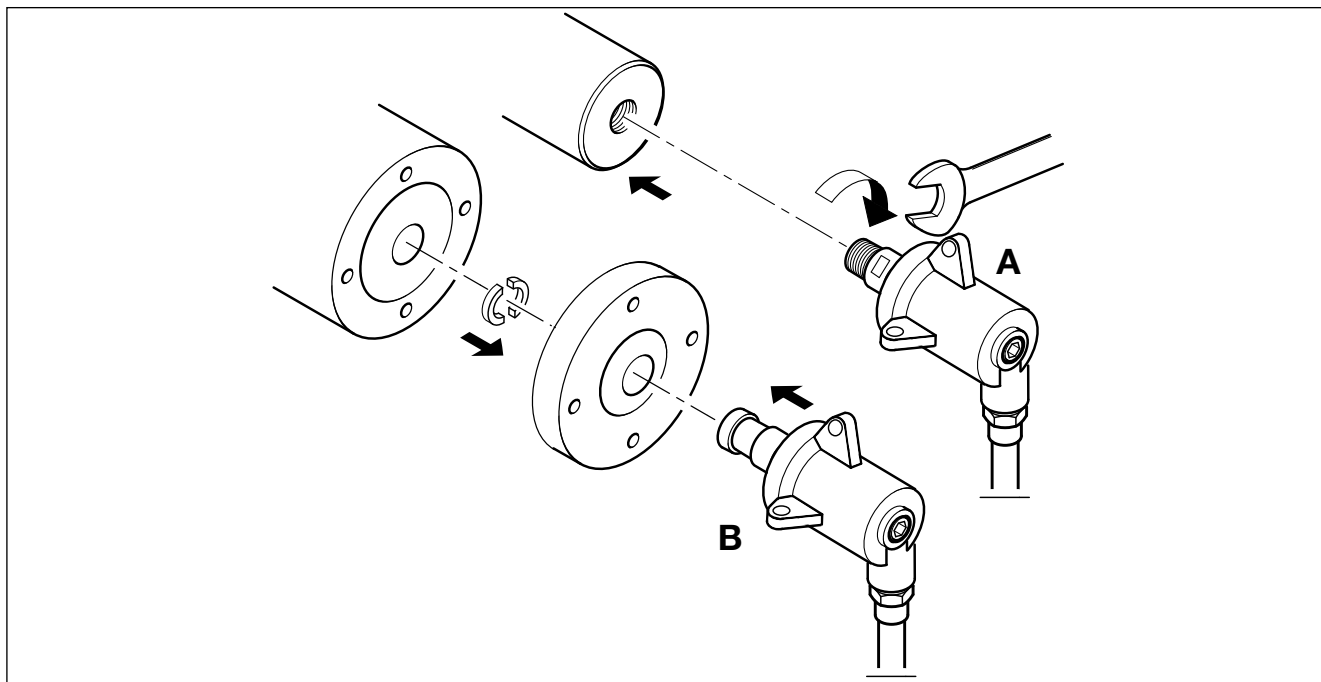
Varianten für die Befestigung an die Maschinenwelle
